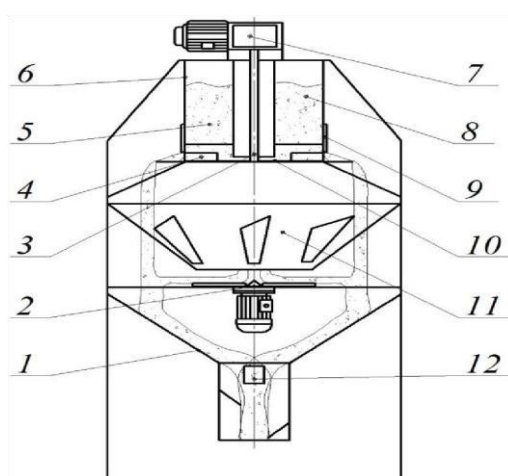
Схема дозатора-смесителя сыпучих кормов: 1 – вторая воронка; 2 – разбрасыватель; 3 – приводной вал; 4 – скребок; 5 – подвижная перегородка; 6 – бункер; 7 – мотор-редуктор привода скребков; 8 – неподвижная перегородка; 9 – манжета; 10 – диск; 11 – первая воронка; 12 – пластины
